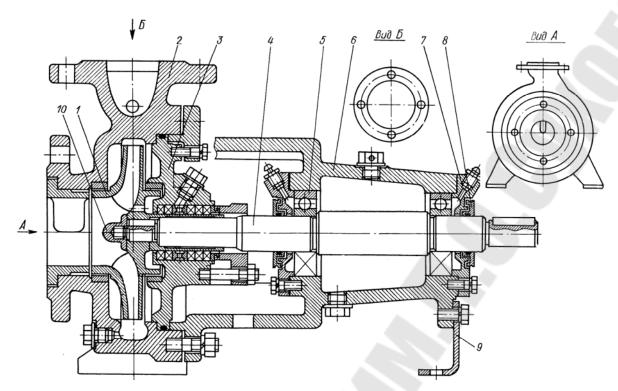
Центробежный одноступенчатый горизонтальный насос типа K: 1 – рабочее колесо; 2 – корпус; 3 – крышка; 4 – вал; 5 – подшипник; 6 – опорный кронштейн; 7 – штуцер; 8 – маслосбрасывающее кольцо; 9 – опорная стойка; 10 – обтекатель
